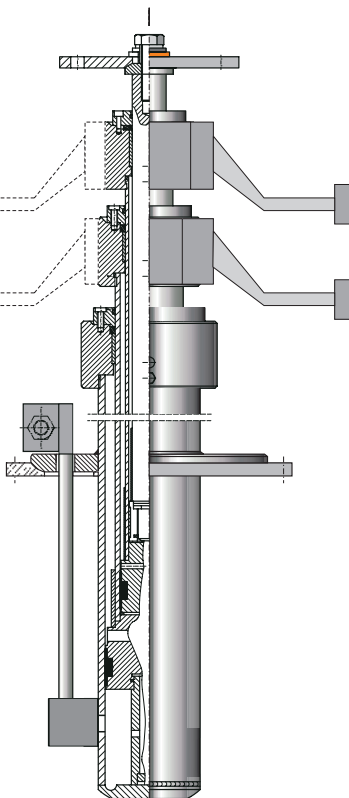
Cilindro telescopico con attacchi e bracci di guida
